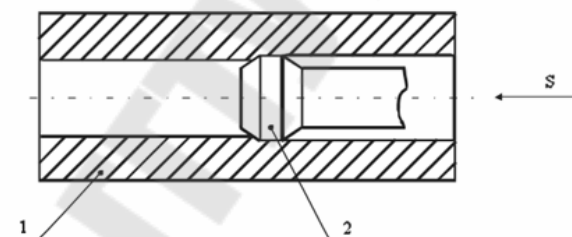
Схема дорнования: 1 – изделие; 2 – дорн; s – направление подачи
